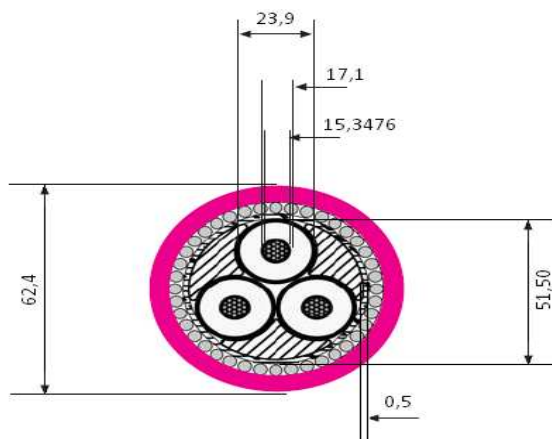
Sección transversal del cable tripolar de potencia con las longitudes expresadas en mm.
